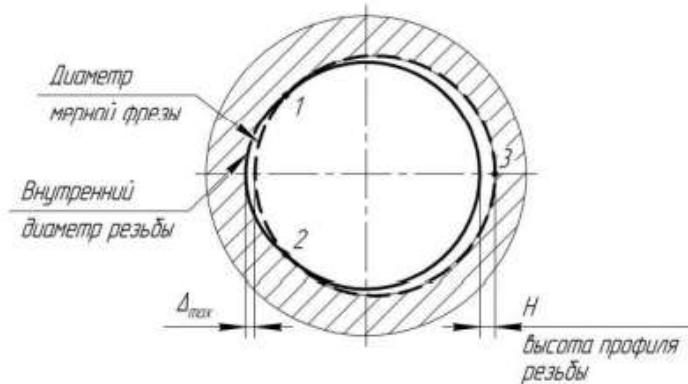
Схематический профиль резьбы в осевом сечении детали
